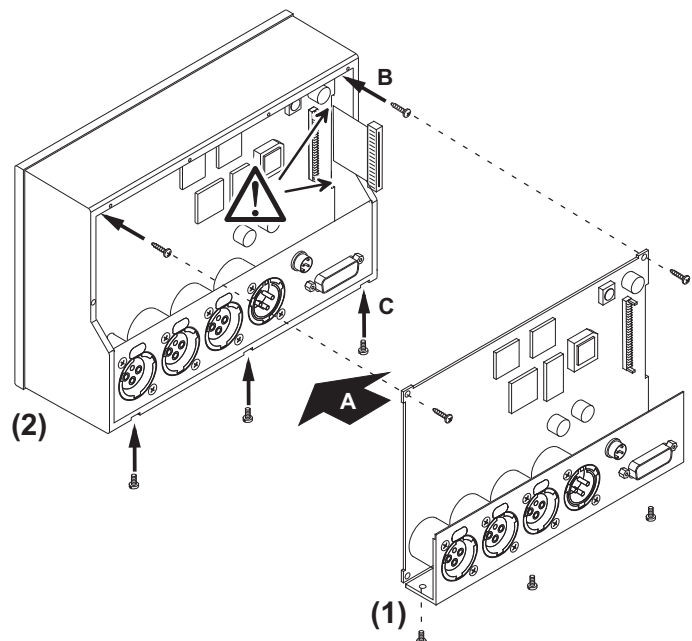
Einbau von Hauptplatine und Anschlusspanel
